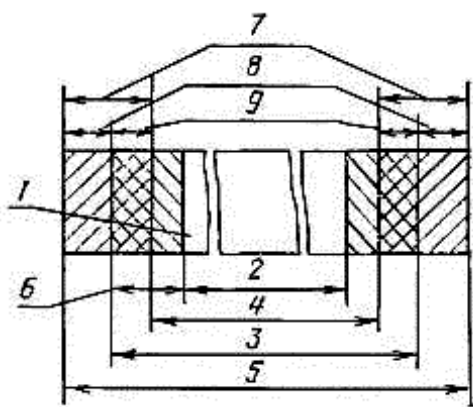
1 - деталь; 2 - размер детали; 3 - номинальный размер поковки; 4- наименьший предельный размер поковки; 5 - наибольший предельный размер поковки; 6 - величина припуска; 7 - допуск (поле допуска); 8 - положительная величина допускаемого отклонения; 9 отрицательная величина допускаемого отклонения.
